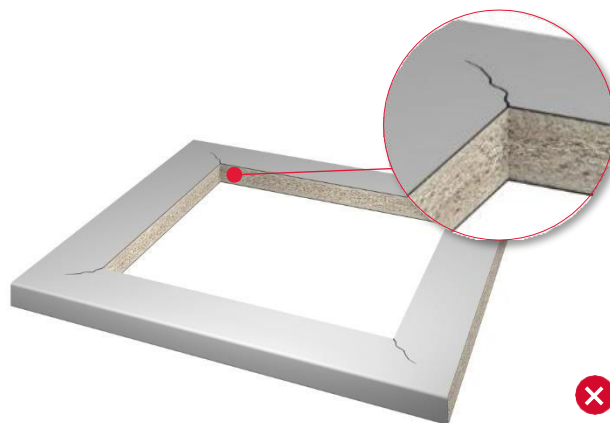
Неправильно – Вырез внутри детали с прямыми внутренними углами
